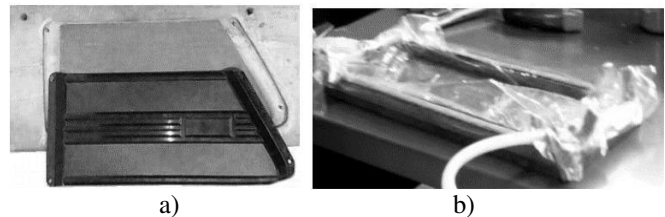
a) Molde del protector lateral. b) Fabricación por inyección de resina. Fuente: Los autores
